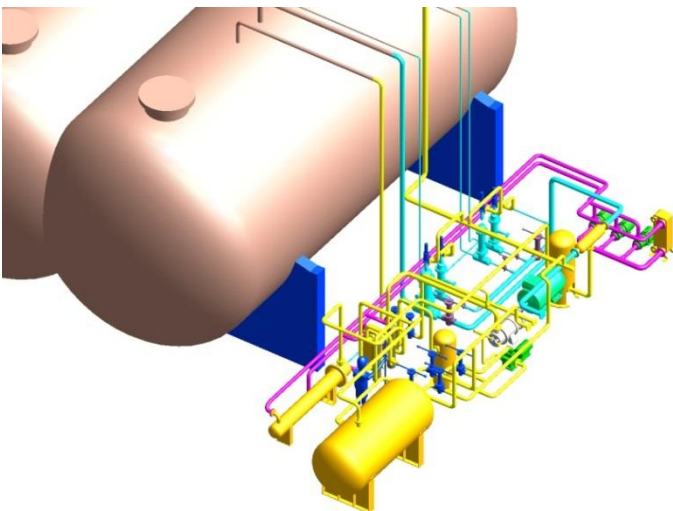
CAD 3-D Ansicht LNG Fuel Gas Supply System der Ro-Pax Ferry
